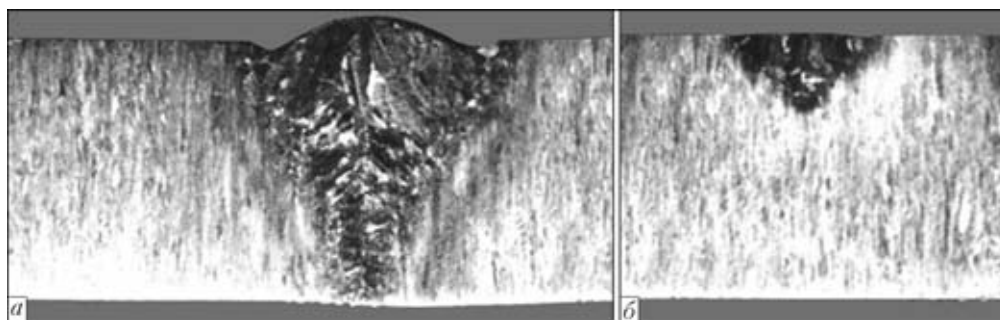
Поперечный макрошлиф наплавки на титановом сплаве ВТ6 толщиной 13 мм: а – лазерно-дуговая сварка, б – лазерная сварка
